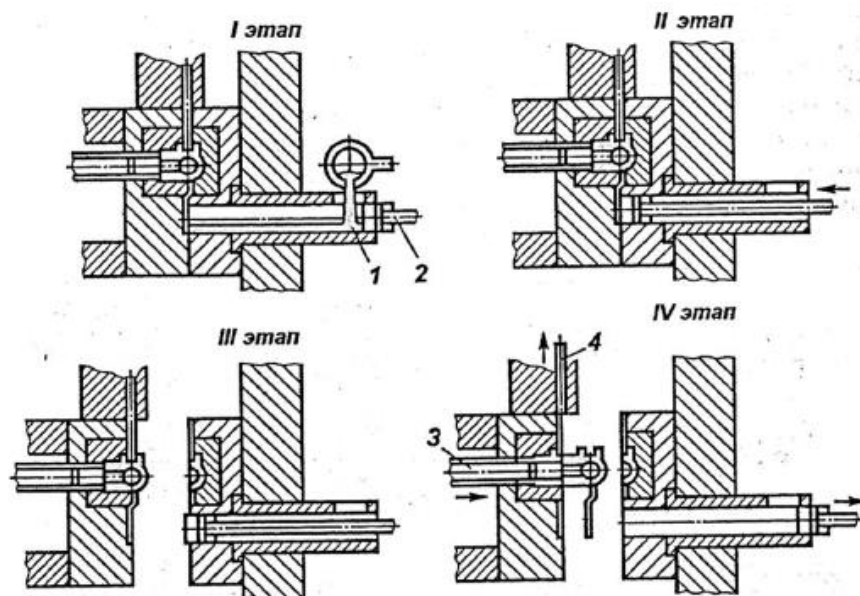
Схема процесса изготовления заготовки литьём под давлением:
